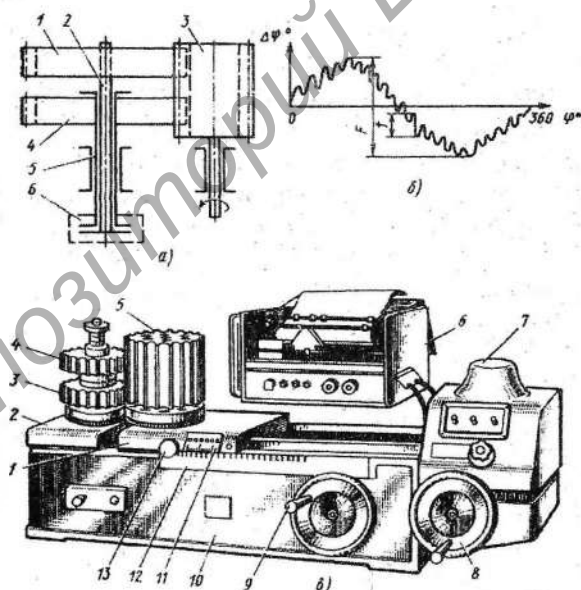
Прибор БВ-608к для измерения кинематической погрешности зубчатых колёс: а — схема измерения; б — диаграмма измерений; в — внешний вид прибора [10, с. 315]
